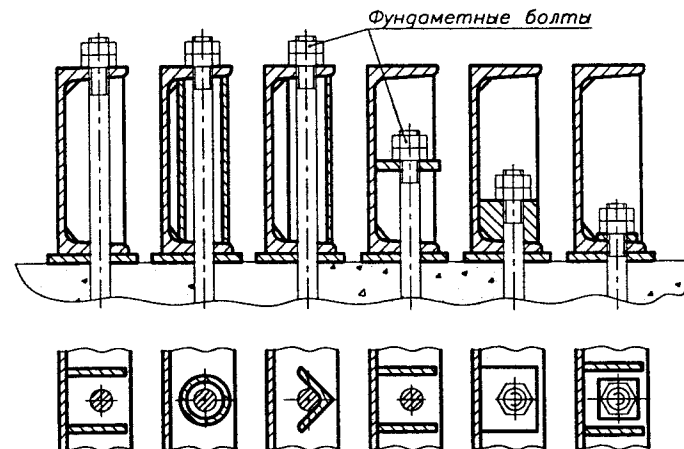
Варианты установки в раме фундаментных болтов
